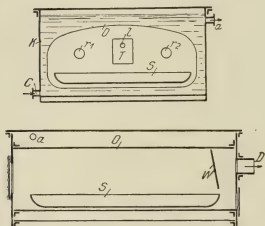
Schwefelofen von FRANK der MASCHINENFABRIK A.-G. VORM. WAGNER & Co., Cöthen.
